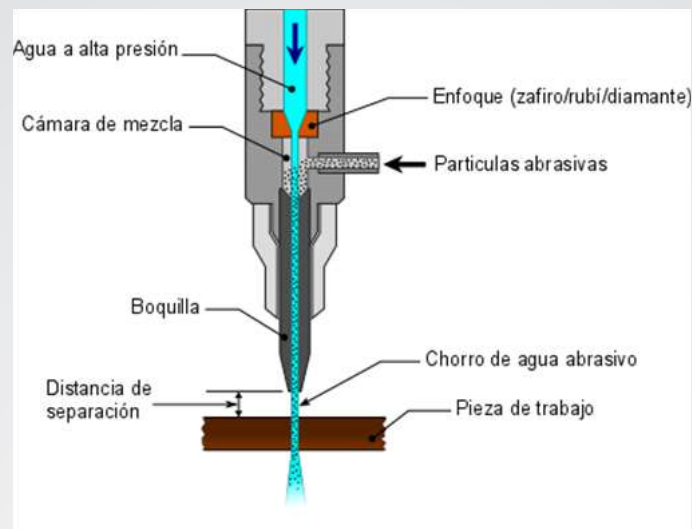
Es quema del conjunto de una boquilla de corte por chorro de agua.
